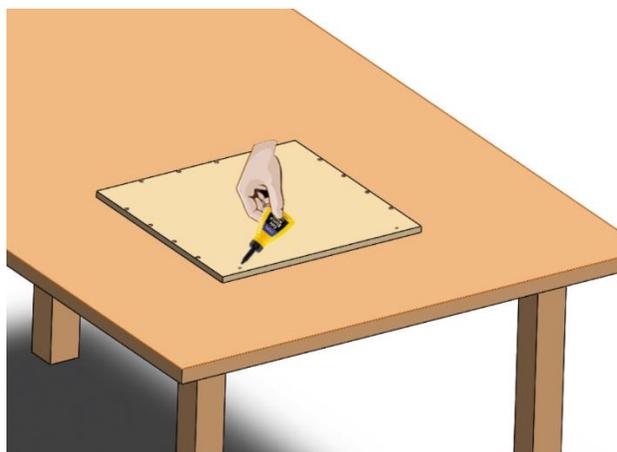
Paso 10 del ensamblaje del cajón (conjunto 2)
